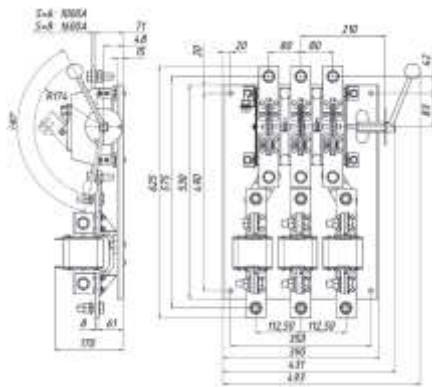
Разъединитель-предохранитель серии РПБ-10, РПБ-16
